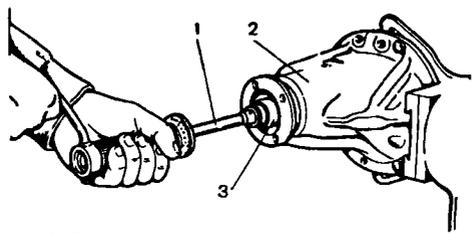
Проверка предварительного натяга подшипников ведущей шестерни: 1 - динамометр 02.7812.9501; 2 - картер; 3 - переходная втулка
